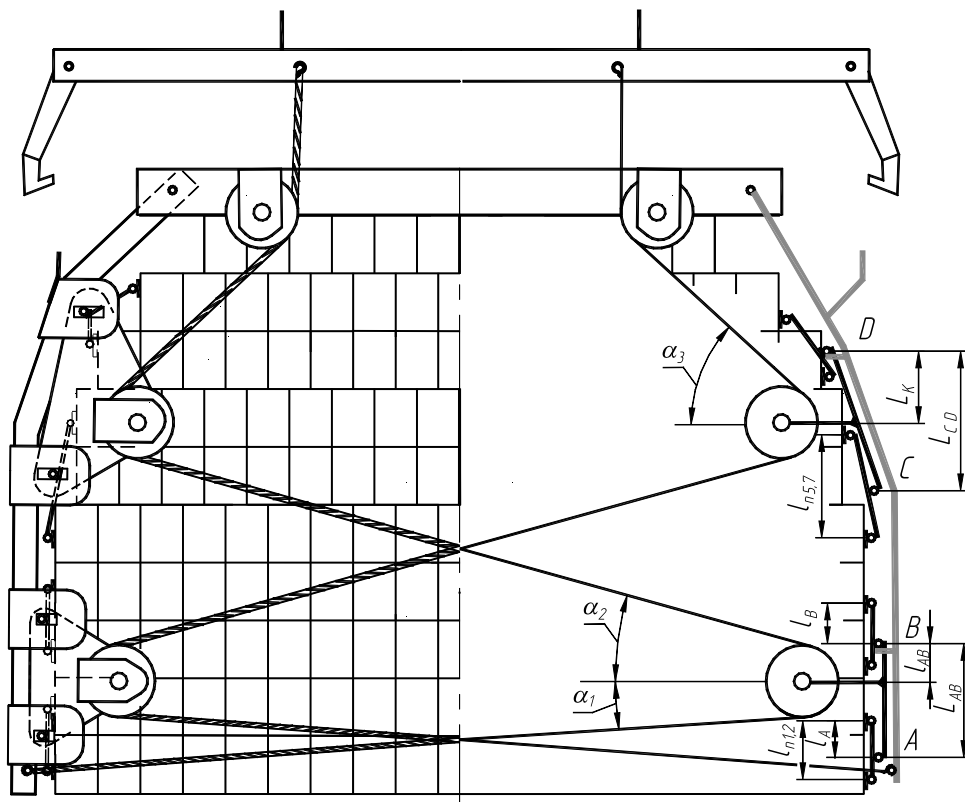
Конструкция и схема механизма уплотнения грузозахватного устройства пакета силикатного кирпича
